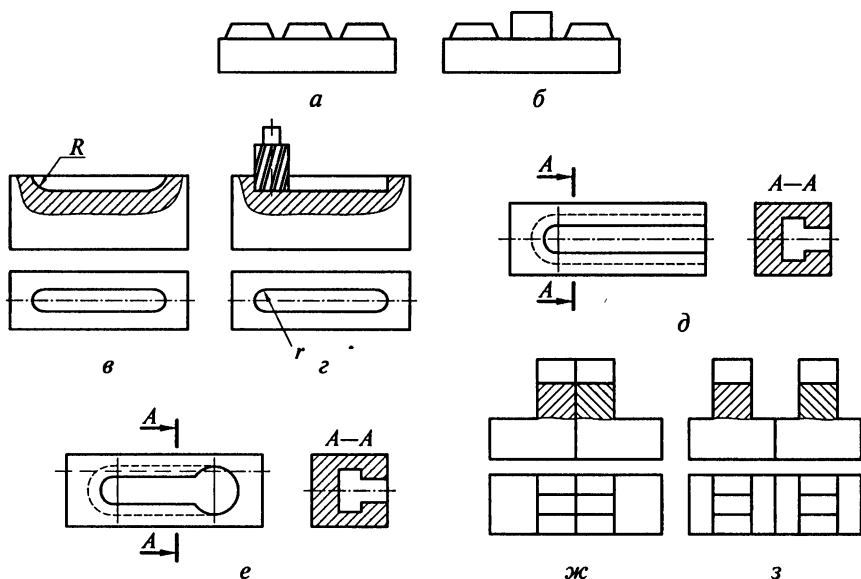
Технологичность конструкций деталей при фрезеровании: *а, д, ж* — технологичные конструкции; *б, е, з* — нетехнологичные конструкции; *в* — паз под дисковую фрезу; *г* — паз под шпоночную фрезу; *г, R* — радиусы пазов
